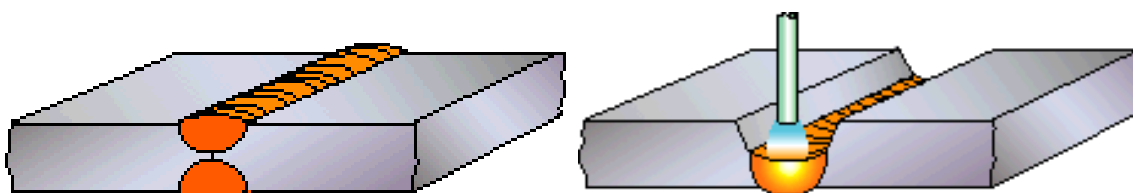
Soldagem dois lados (esquerda) e Soldagem Unilateral (direita)
